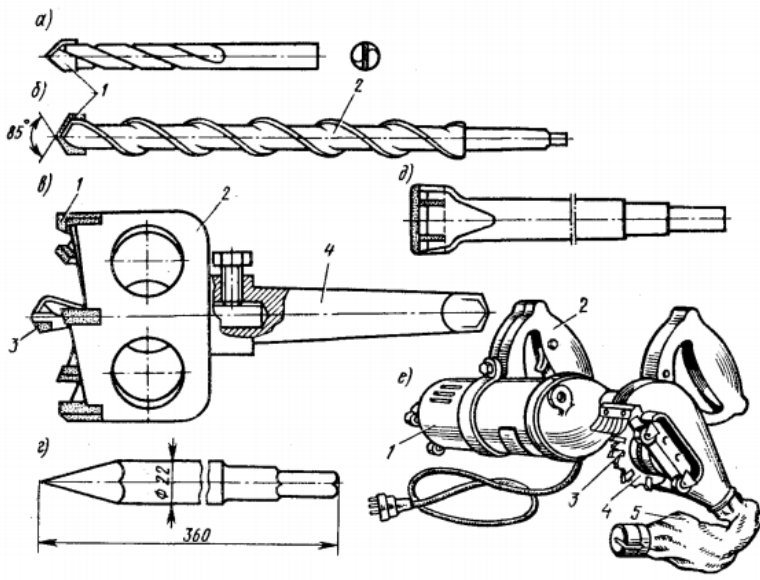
Інструмент для пробивання отворі, ніш і борозен:
